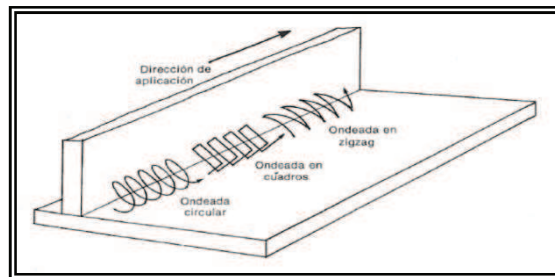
Movimientos de la soldadura ondeada.
